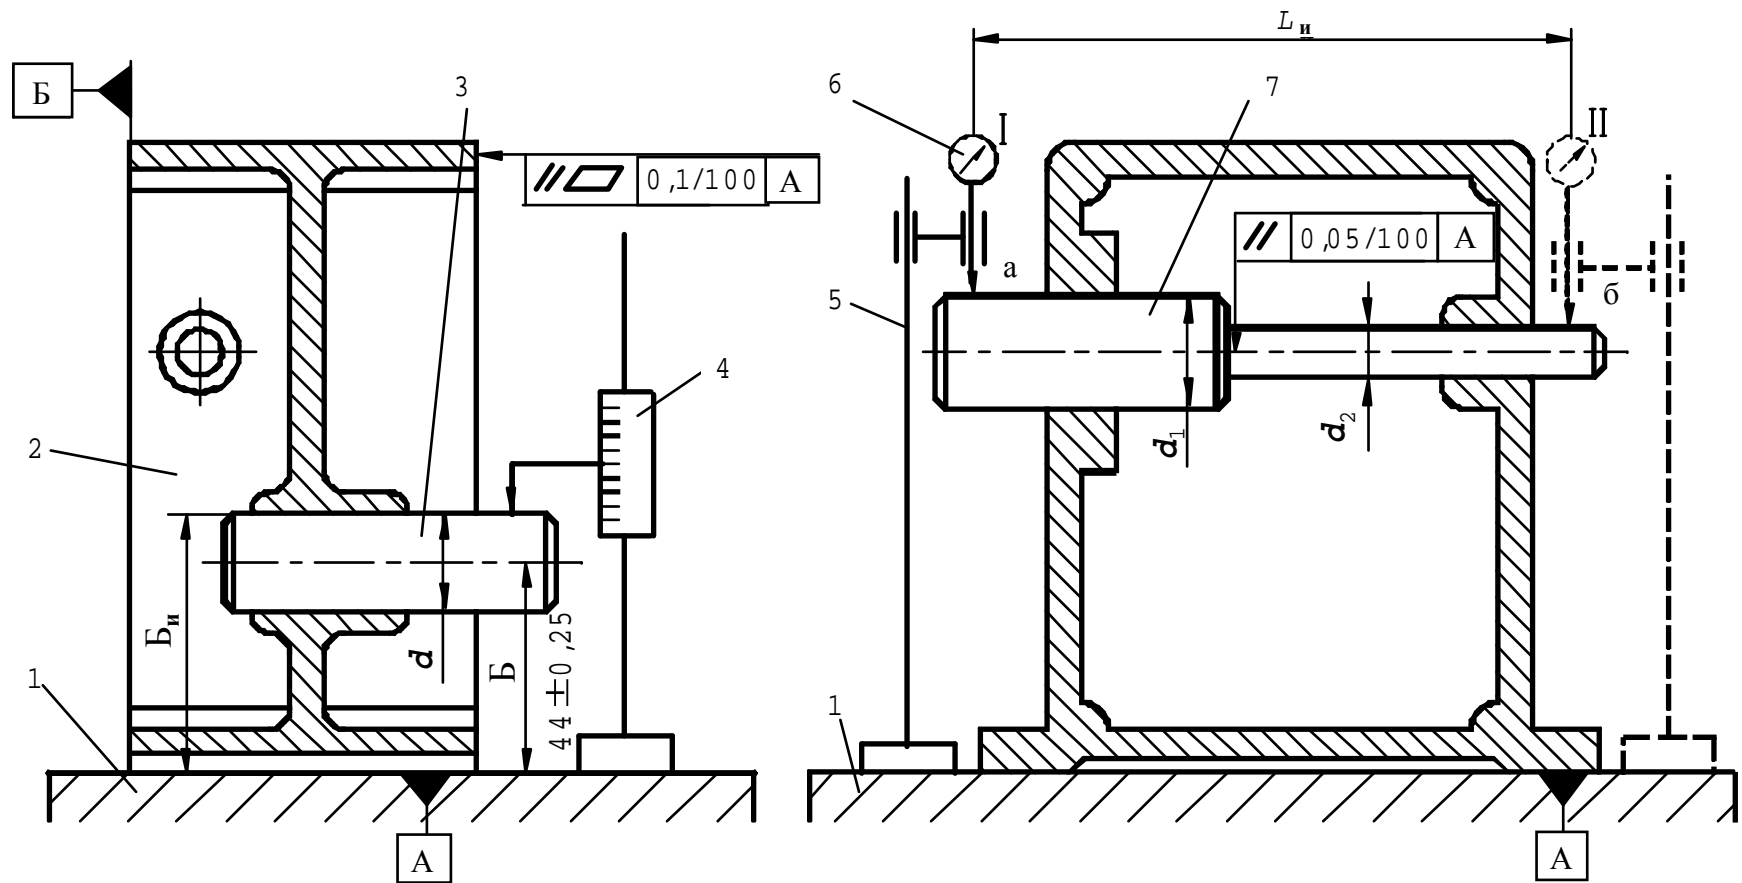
Измерение параметров точности корпуса редуктора: 1 – поверочная плита; 2 – измеряемая деталь; 3, 7 – оправки; 4 – штангенрейсмас; 5 – штатив; 6 – индикатор
